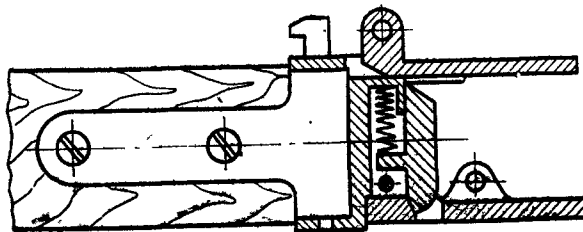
Крепление приклада пулемета РПКС (вид сверху)
